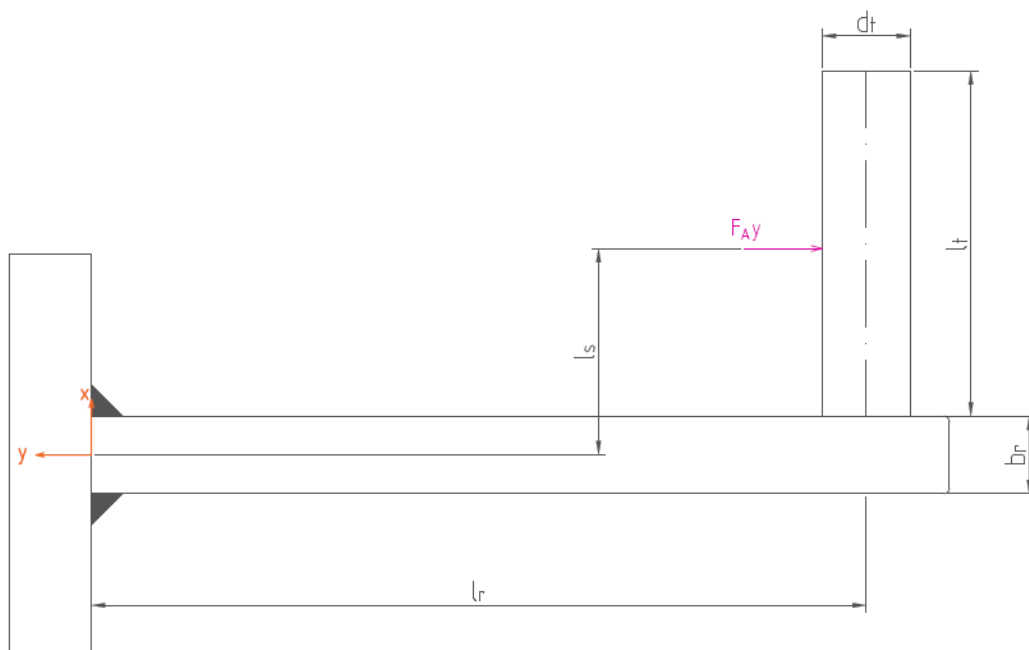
Sklopení průřezu svaru B do roviny připojení
